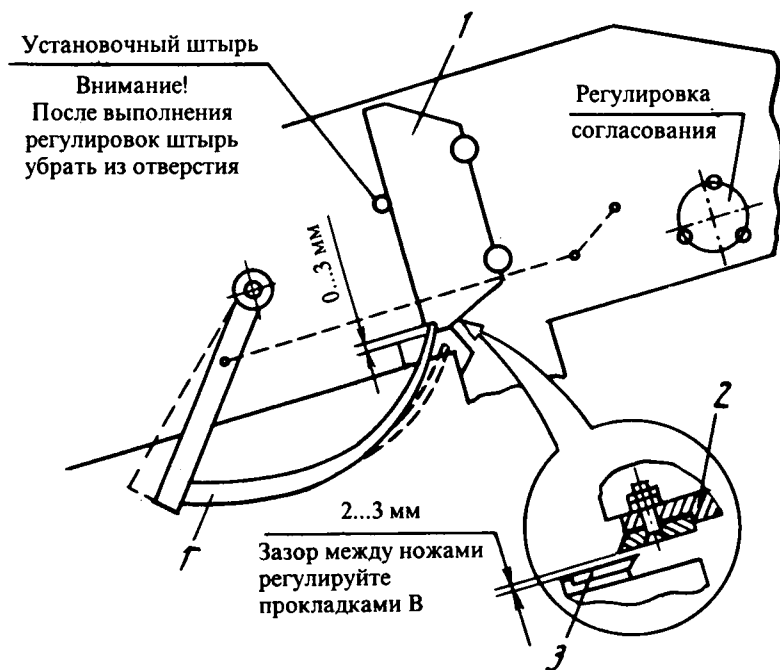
Регулировка зазора между ножами поршня и прессовальной камеры: 1 - нож поршня; 2 - прокладки; 3 - нож прессовальной камеры
